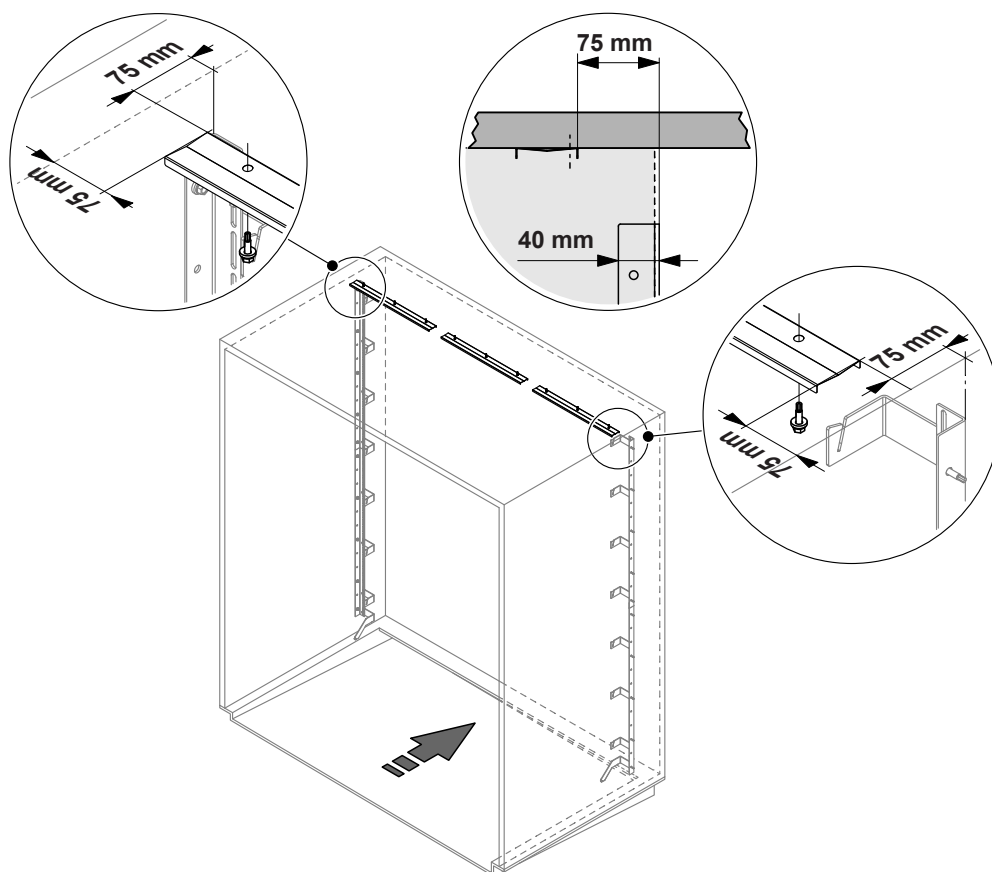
Montage des profils de fixation pour la fixation des tôles d'étanchéité supérieures
